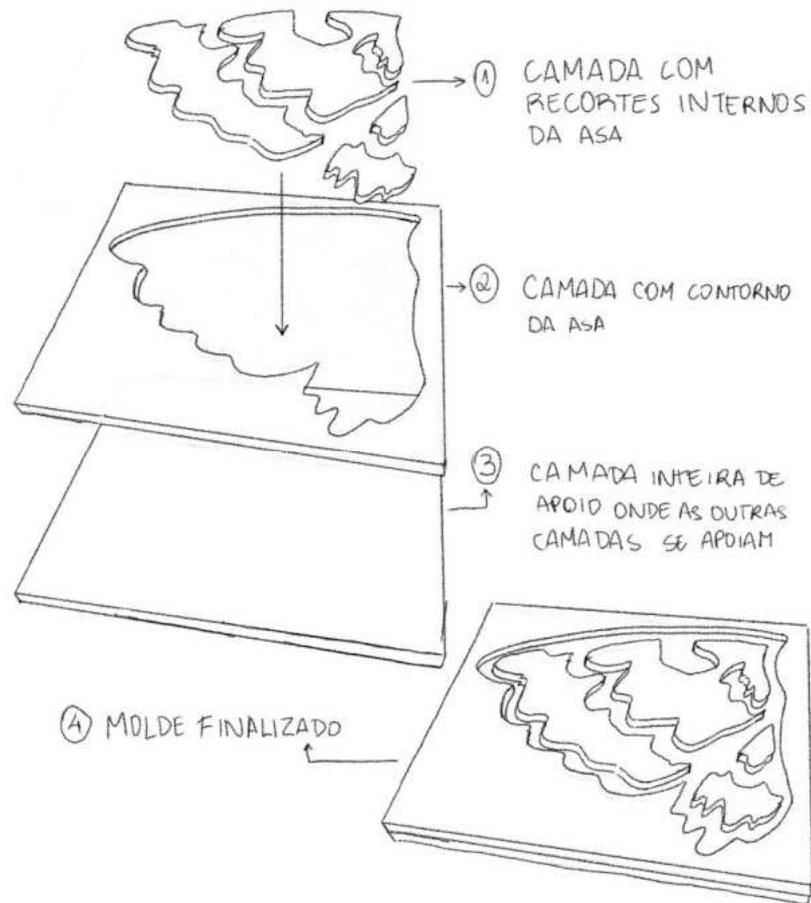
Passo-a-passo de montagem dos moldes recortados à laser em placa de acrílico de 2mm. Fonte: a autora.
